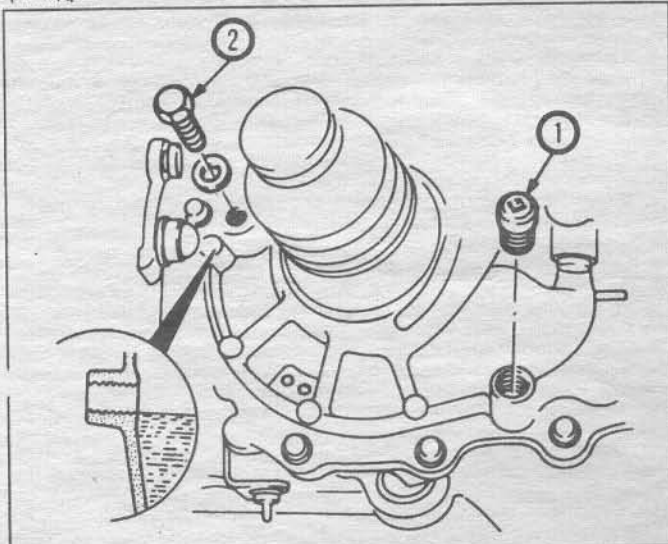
Сливная (1) и заливная (2) пробки механической коробки передач.
